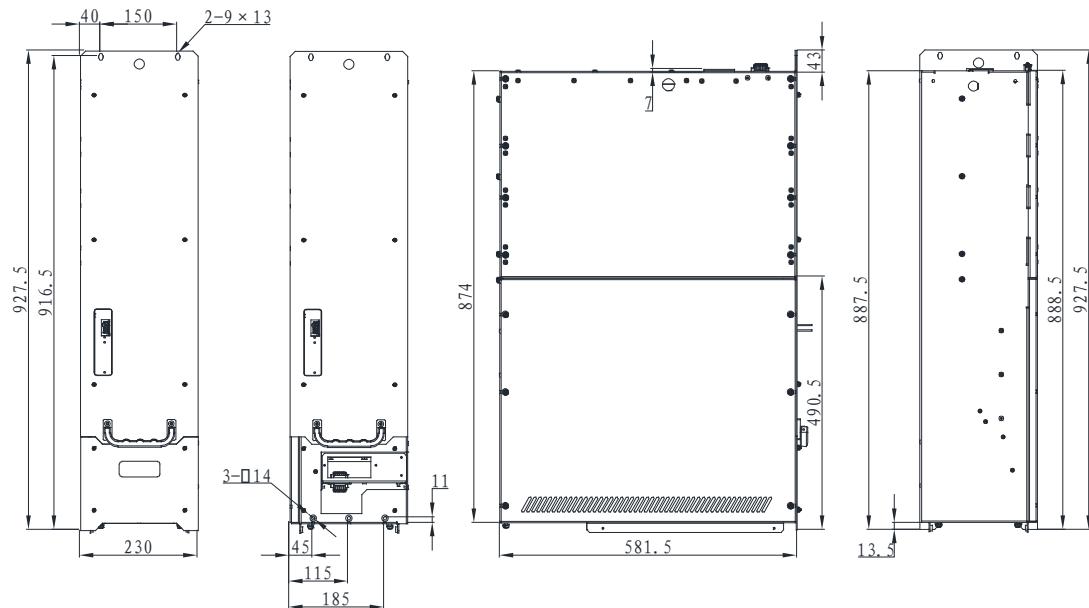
H8A逆变模块外形尺寸 (单位: mm)
